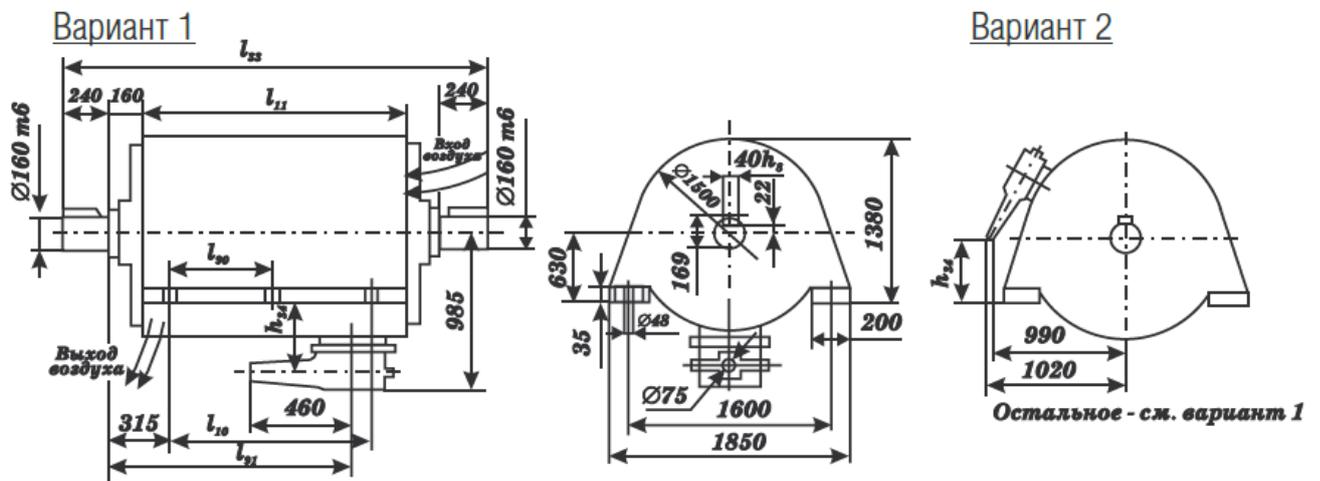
Габаритные, установочные размеры двигателей СДЭ2 16-го габарита напряжением 6 кВ
